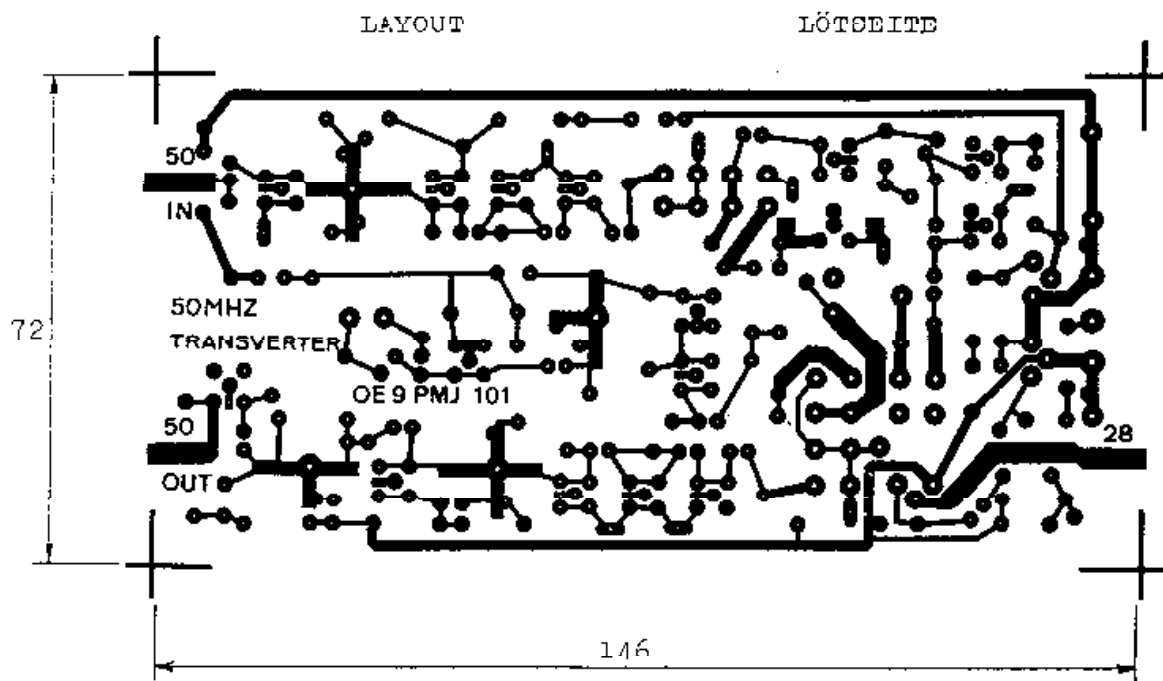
/ Figure 5: Gedruckte Schaltung/PCB
